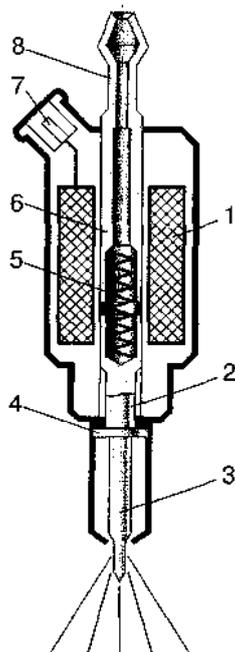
Конструктивная схема электромагнитной форсунки: 1 - обмотка электромагнита; 2 - якорь; 3 - запирающий элемент; 4 - упор; 5 - пружина; 6 - магнитопровод; 7 - выходные контакты; 8 - штуцер для топлива
